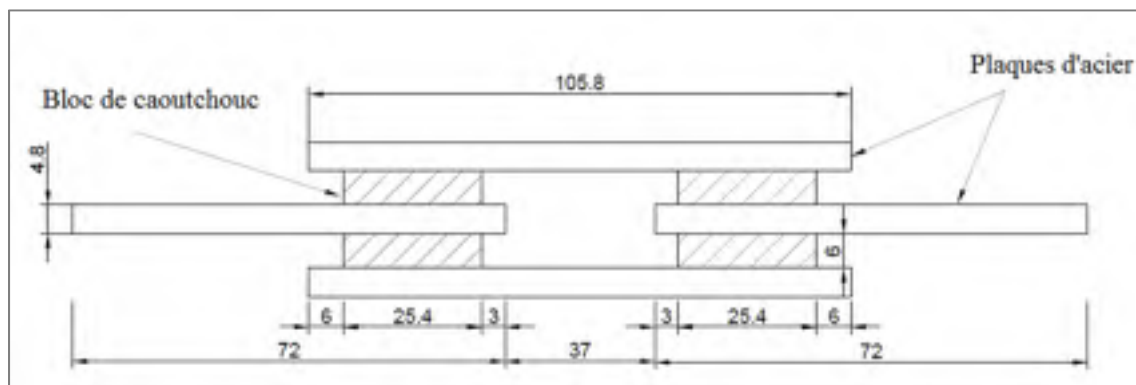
Plan montrant les dimensions des spécimens d'essai (mm)
